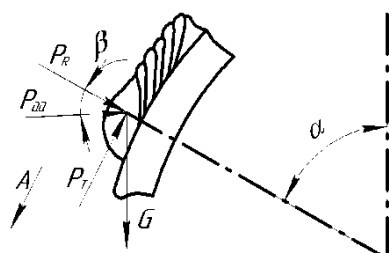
Схема сил, действующих на сварочную ванну
